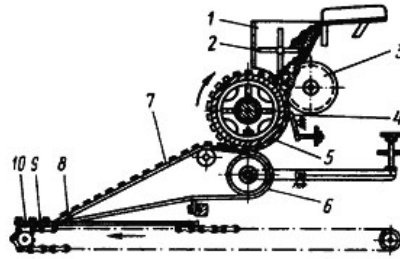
Схема ротационной формующей машины: 1—бункер; 2—защитная крыльчатка; 3—питающий барабан; 4—нож; 5—формующий барабан; 6—натяжной ролик; 7—движущий тканевой транспортер; 8—ножевая планка; 9—цепной транспортер; 10—металлический трафарет.
